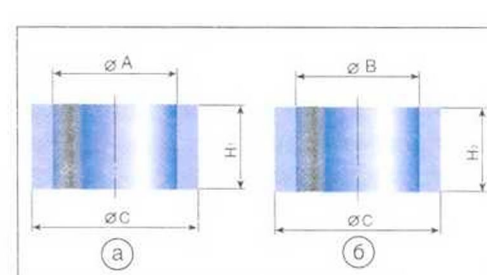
Оправка (а) и кольцо (б) для разборки и сборки карданной шарниры
